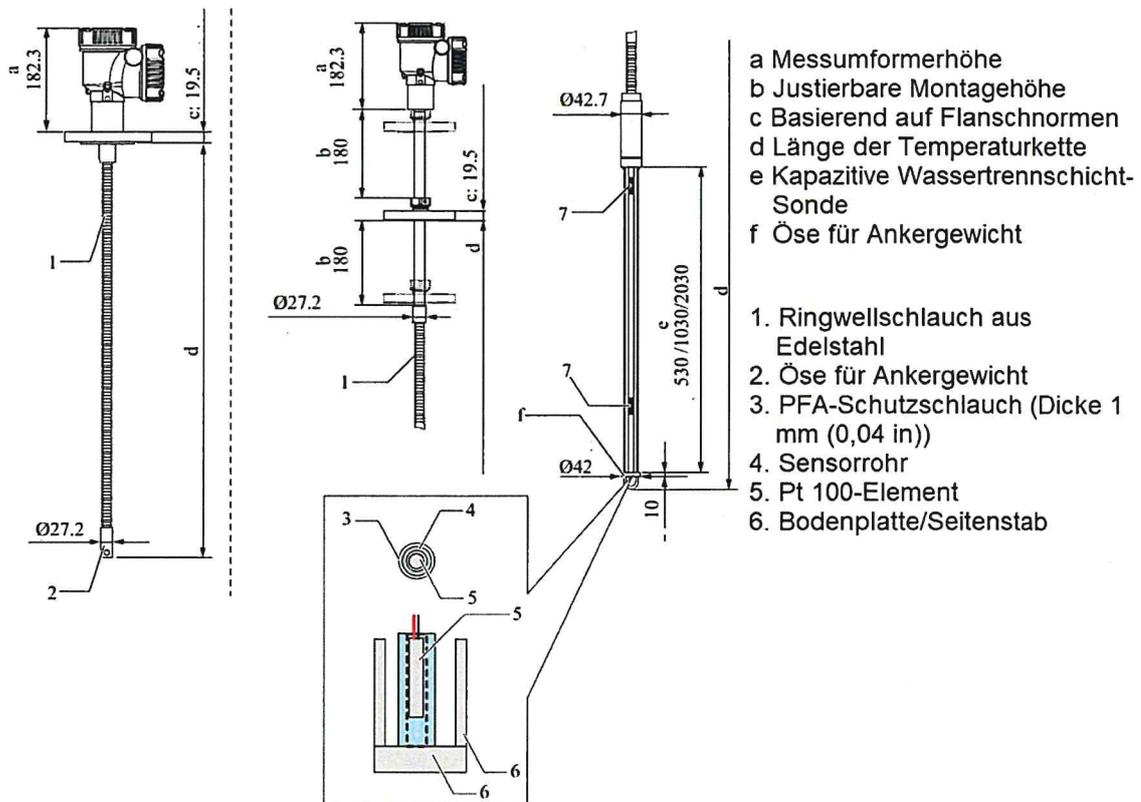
Prothermo NMT81 in den Ausführungen (von links): mit verschweißten Flansch, mit einstellbarem Flansch, mit Wassertrennschichtmessung.
